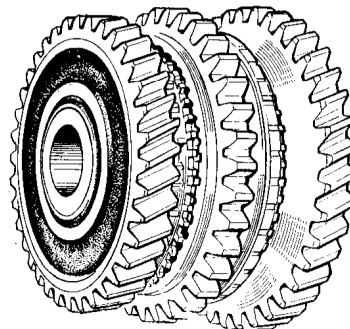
Ступица муфты синхронизаторов I и II передач с муфтой включения синхронизаторов и набором шестерен (перед установкой в картер коробки передач)
